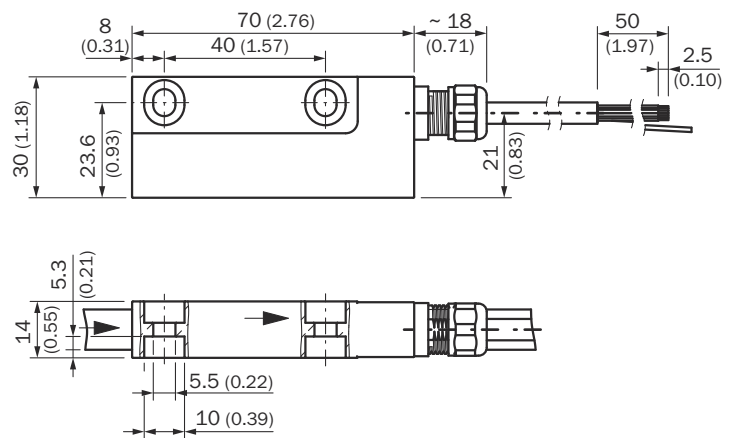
Disegni quotati TTK70S con uscita del cavo (tutte le dimensioni in mm)
